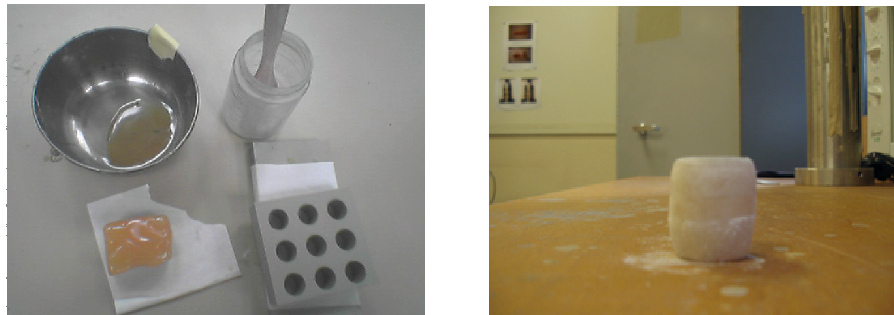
(a) Bloc de colle, récipient servant à recueillir la colle fondue, et moule de forme cylindrique (b) Exemple de lopin obtenu par moulage.
